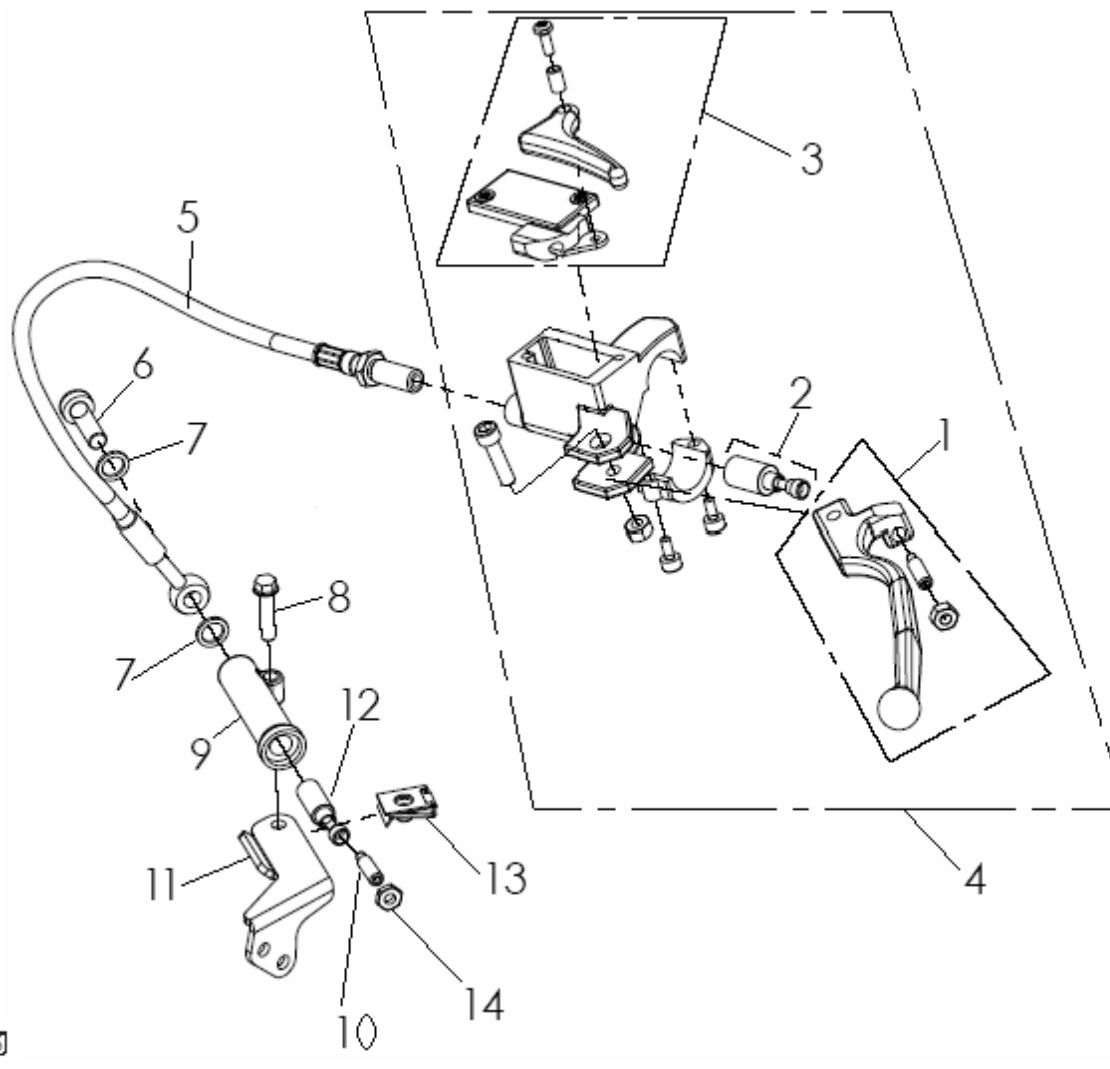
LEVIER D'EMBRAYAGE / CLUTCH LEVER / MANETA DE EMBRAGUE
